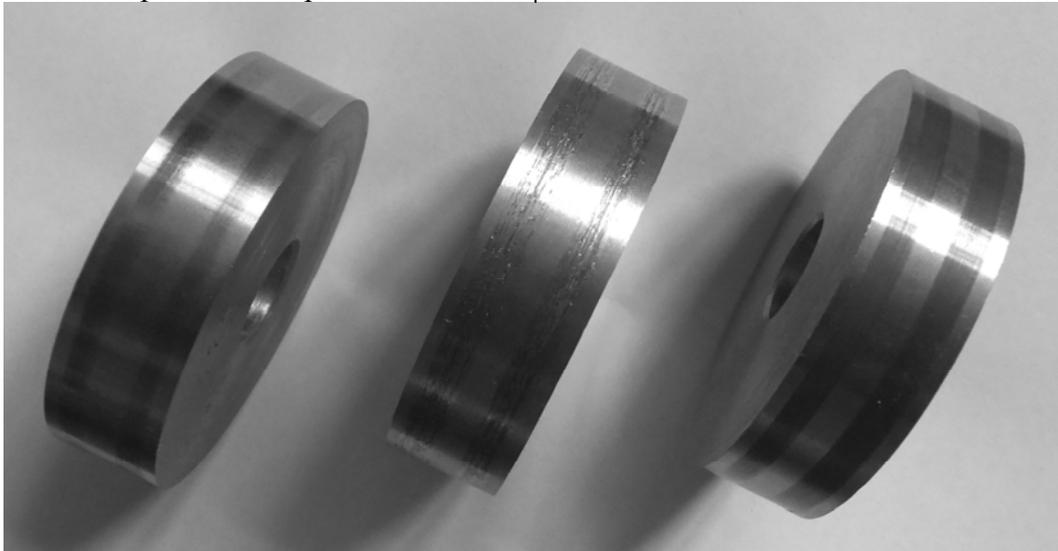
Внешний вид стальных образцов после триботехнических испытаний: слева – образец из стали 35ХГСА (HRC 40...45), по центру – из стали 12X18H10T (HB 190...210), справа – из стали 45 (HB 200...220) с темными оксидными пленками на поверхностях трения
